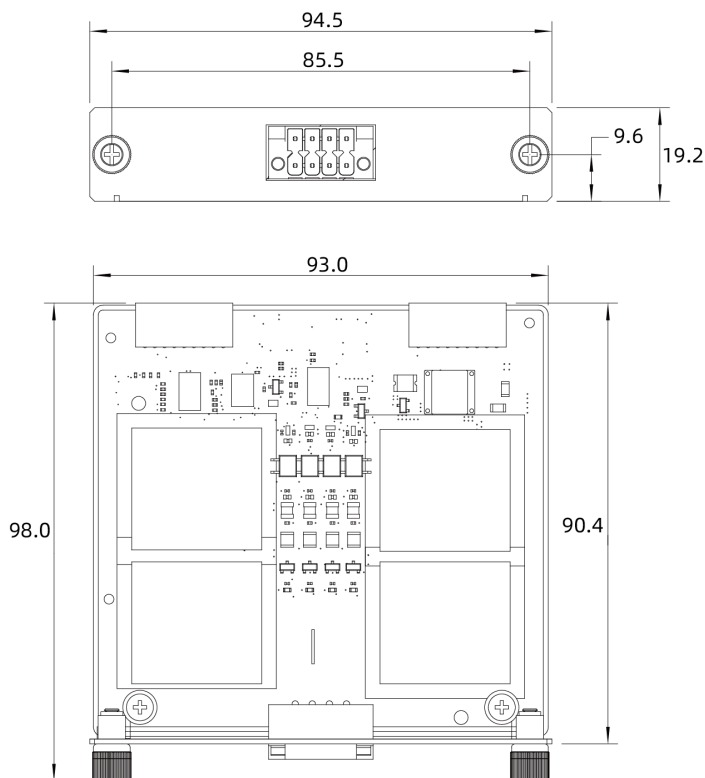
安全RO扩展卡尺寸图 (单位: mm)
